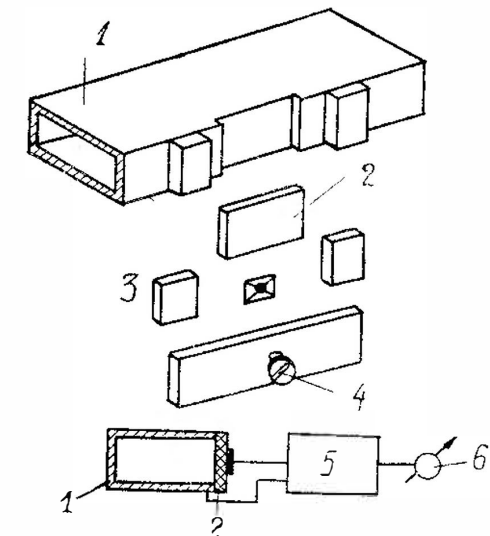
Схема и конструкция индикаторного устройства с пьезокварцевой пластинкой.
